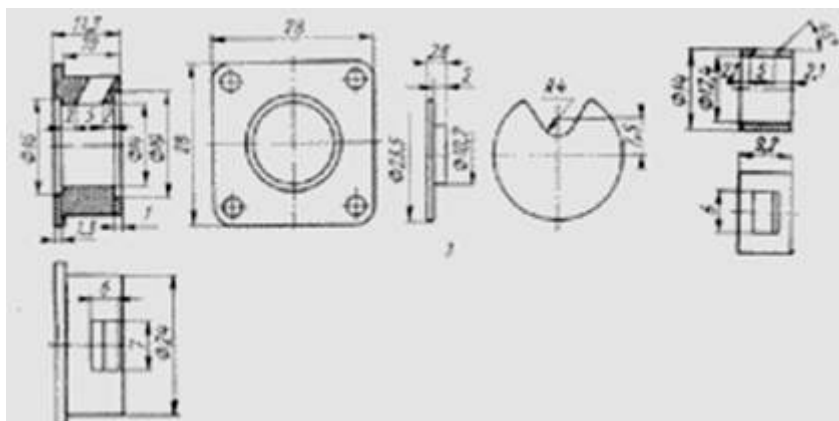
Изготовление втулки и вставка ее в заднюю стенку.
